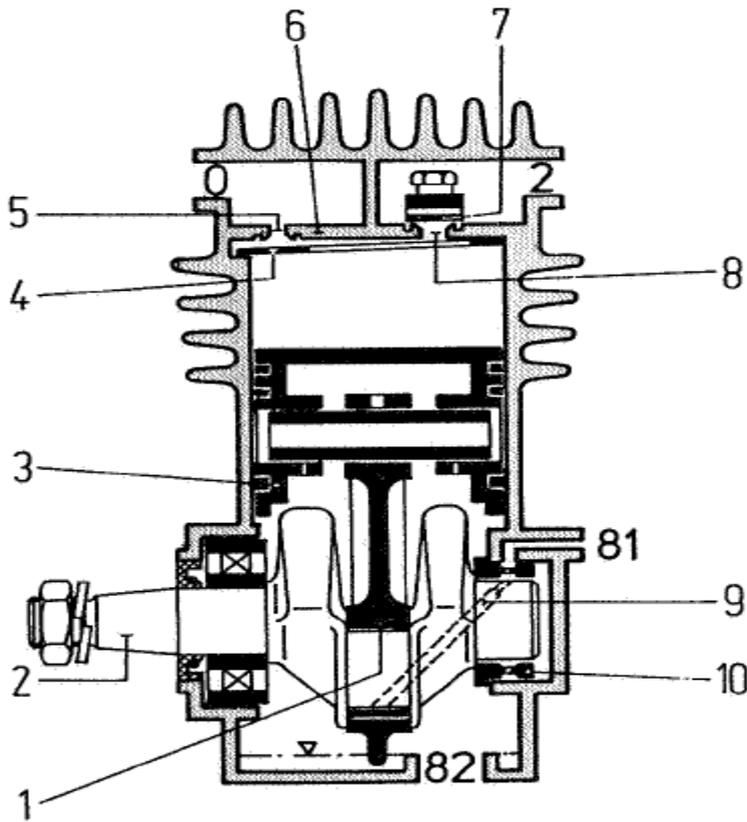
Vue éclatée d'un compresseur. [8]
